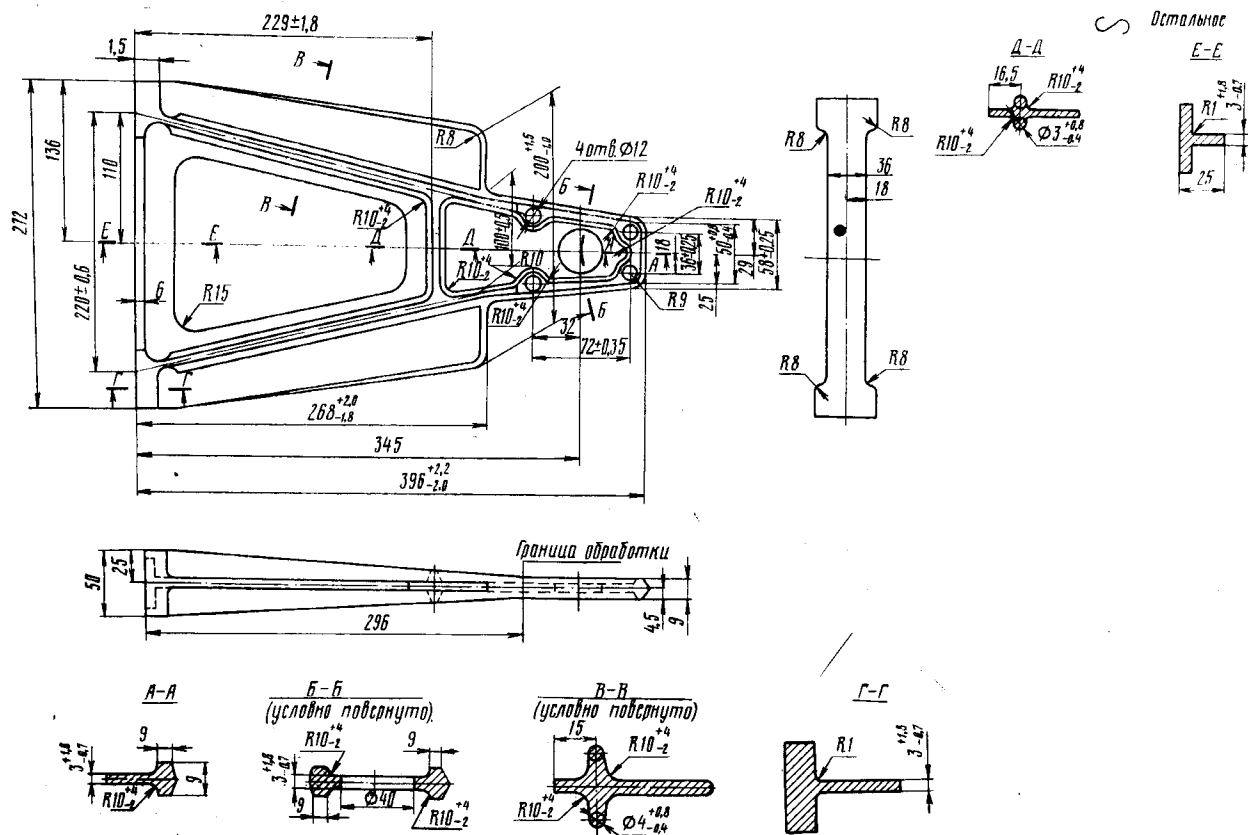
Пример оформления чертежа детали, изготовленной из штампованной заготовки.
